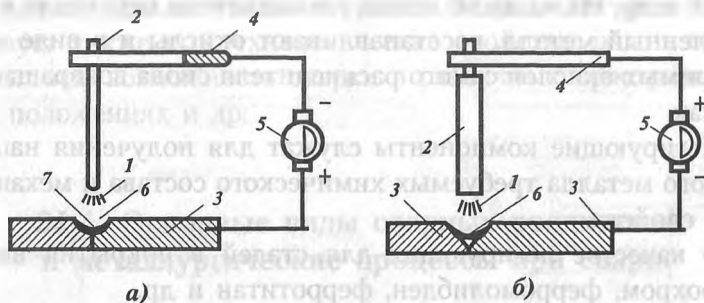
Схема ручной электродуговой сварки: 1 — электрическая дуга; 2 — металлический электрод; 3 — изделие; 4 — держатель; 5 — генератор тока; 6 — сварочная ванна; 7 — присадка
